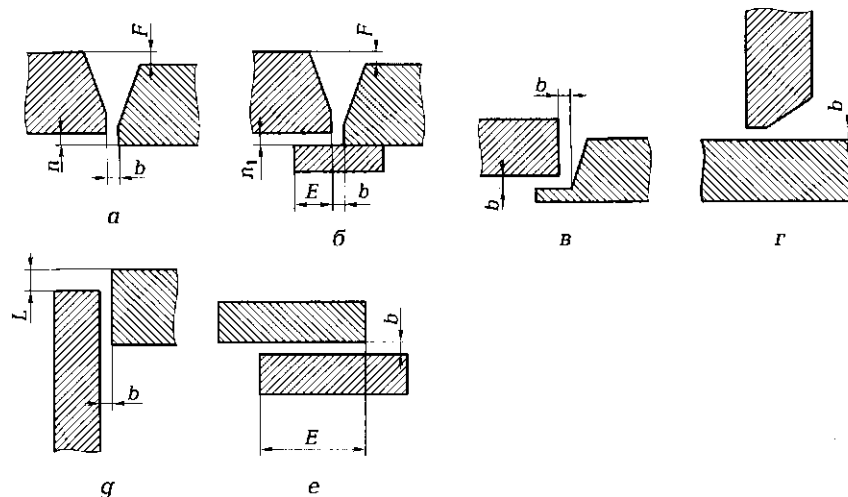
Размеры, контролируемые при сборке под сварку соединений разных типов:
